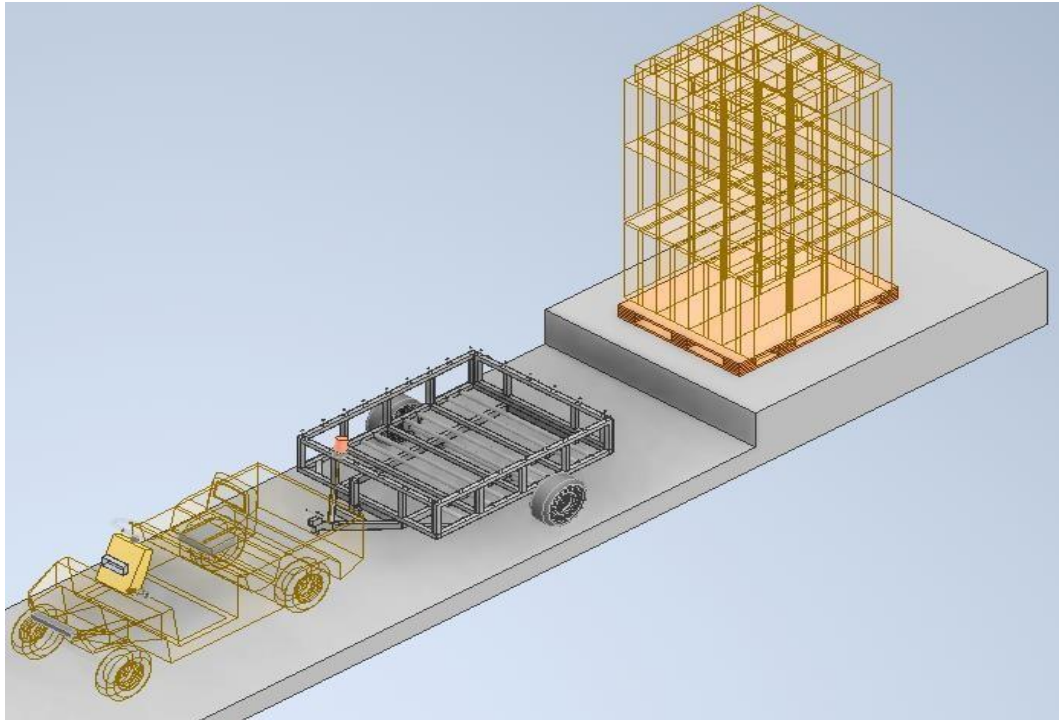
Diseño del remolque anclado al remolque, en la bahía de carga del pallet.
